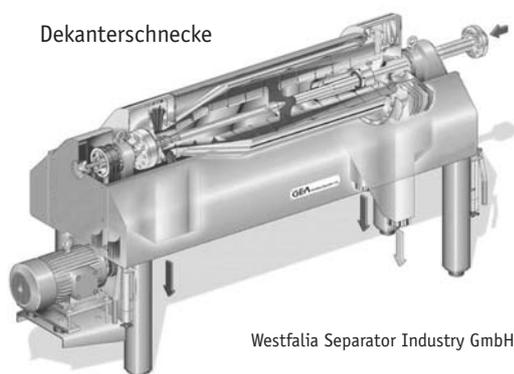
Hoch belastete Baugruppen der Förder- und Extrusionstechnik
